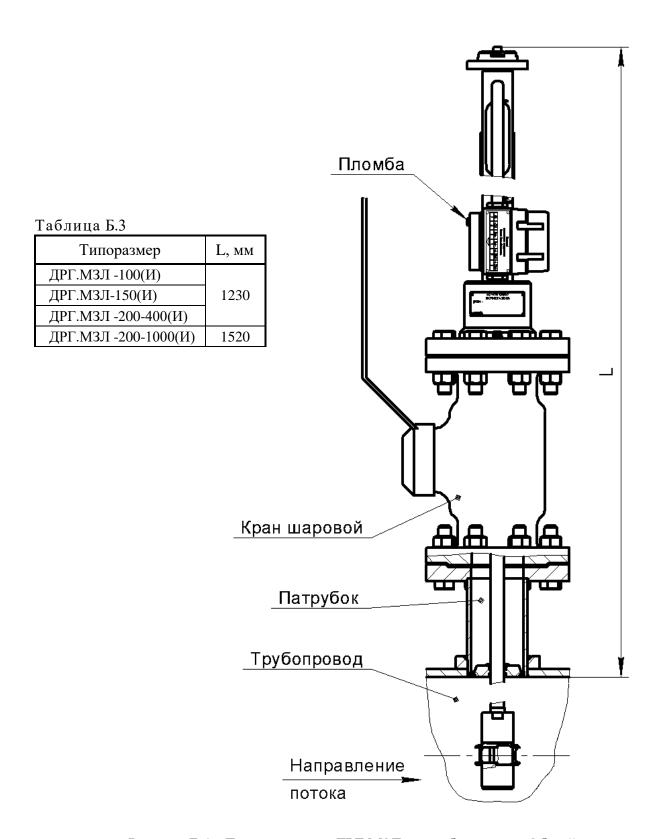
Датчик расхода ДРГ.МЗЛ на трубопроводе. Общий вид
